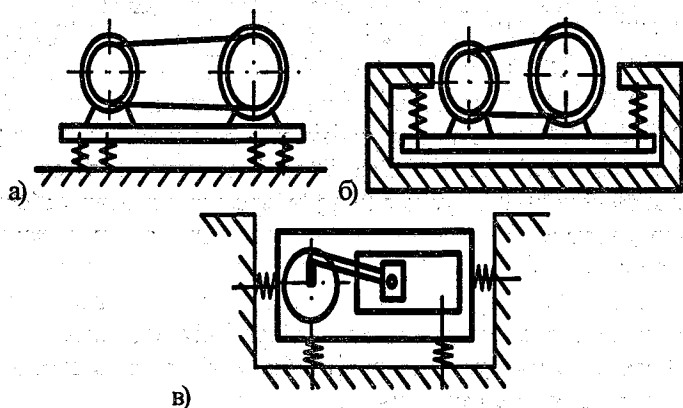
Схема виброизоляции виброактивного оборудования: а) опорный вариант; б) подвесной вариант; в) виброизоляция вертикальных и горизонтальных колебаний
